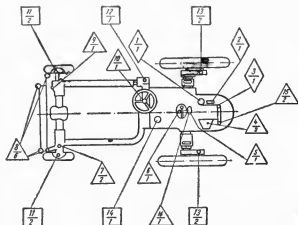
Схема смазки самоходного шасси ДВСШ-16:
